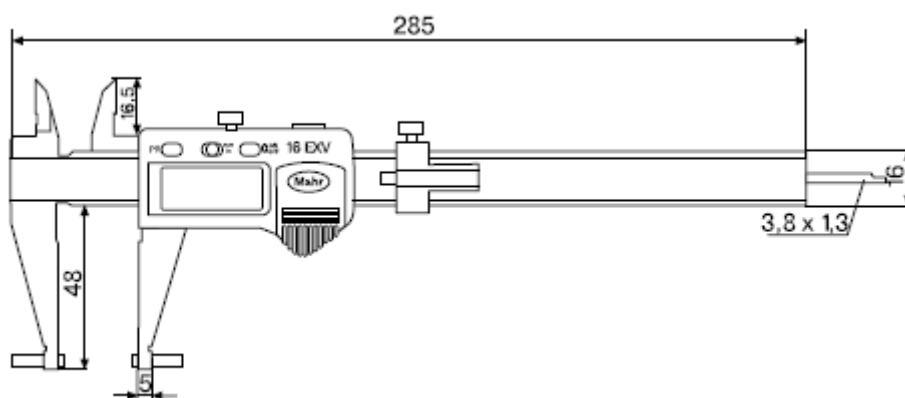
Штангенциркуль универсальный 16 EXV
